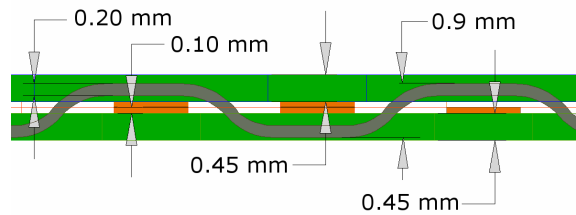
Coupe latérale du composant qui montre les dimensions prévues pour l'épaisseur des PCBs et des pistes de cuivres. Le noyau ne dépasse pas du PCB.
